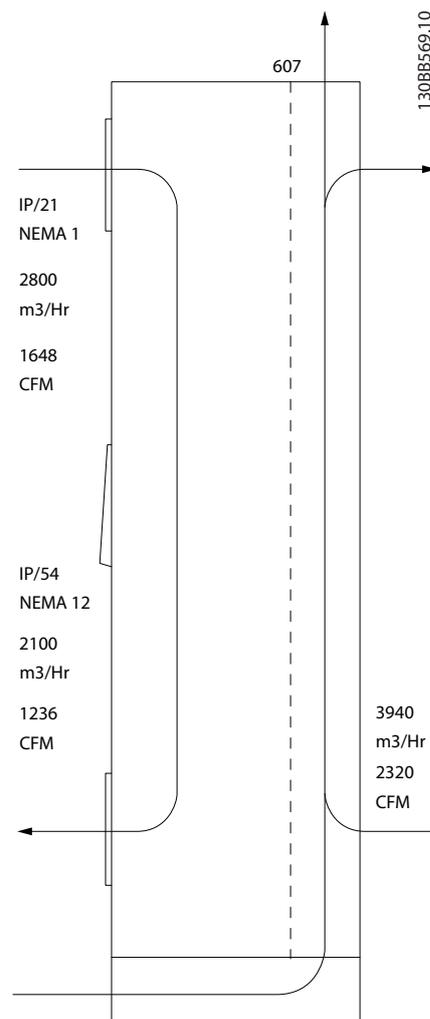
Dimensões Mecânicas (mm), F10
